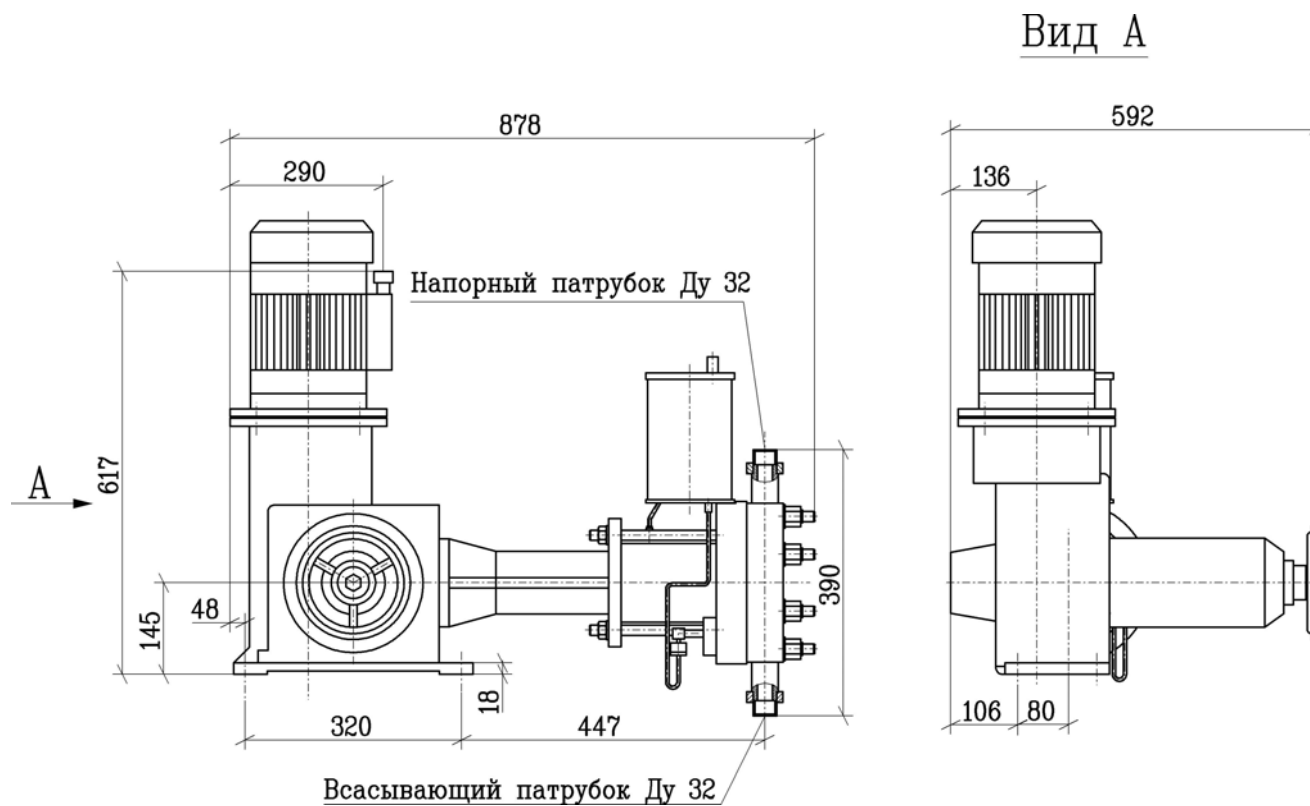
Габаритный чертеж насоса-дозатора гидразина QCE10AP001, QCE10AP002
